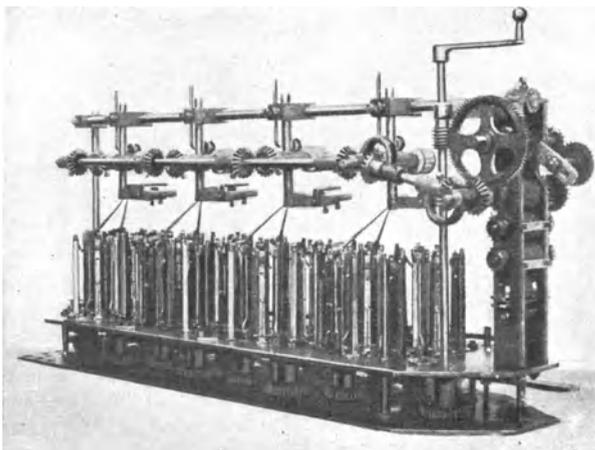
Vierköpfige Gummilitzenmaschine mit Zahnradantrieb für den Aufnehmer.
